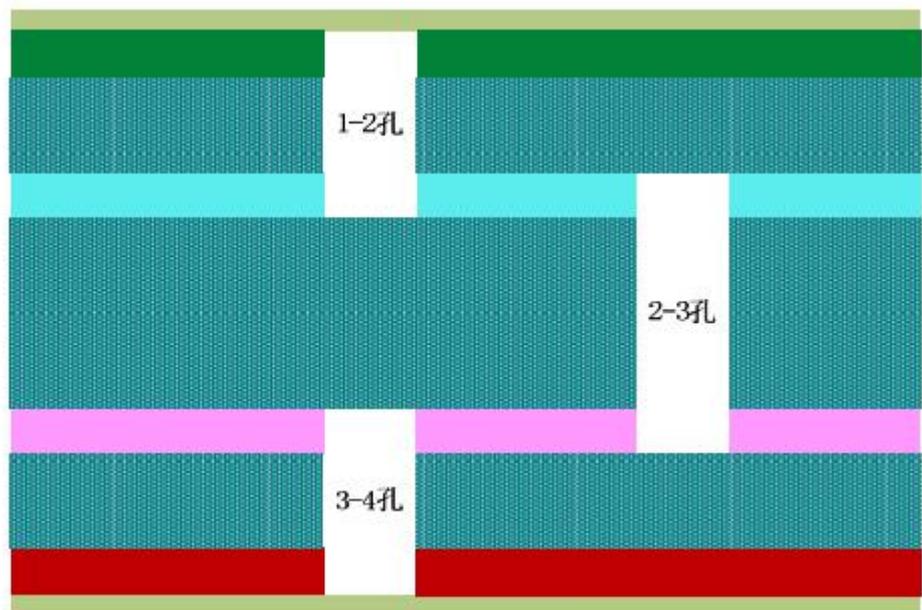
1mm 厚盲埋孔 PCB 板叠层示意图
